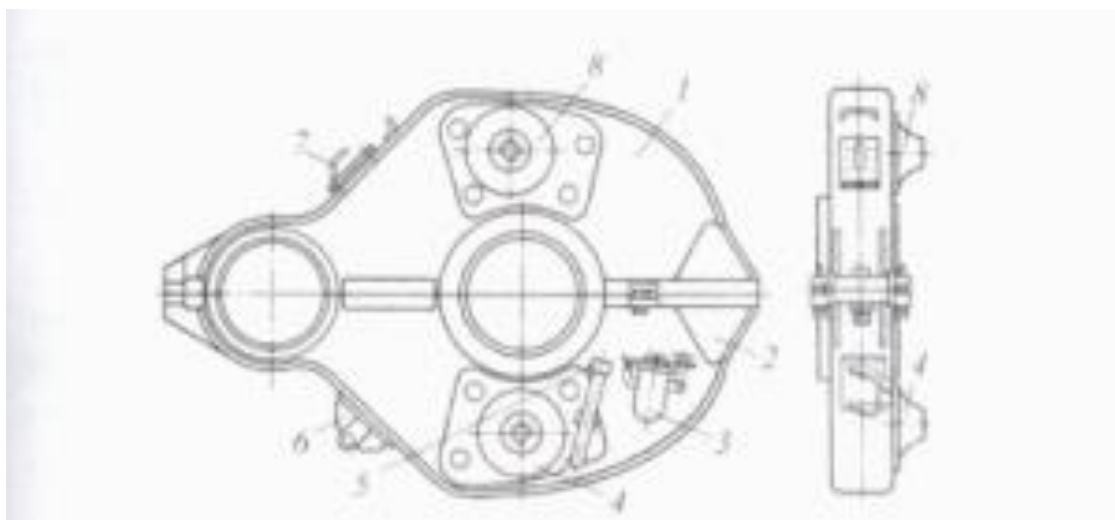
Кожух зубчатой передачи: 1,2 — верхняя и нижняя половинка кожуха; 3 — масленка; 4, 8 — бобышка; 5 — указатель уровня масла; 6 — кронштейн; 7 — сапун.
